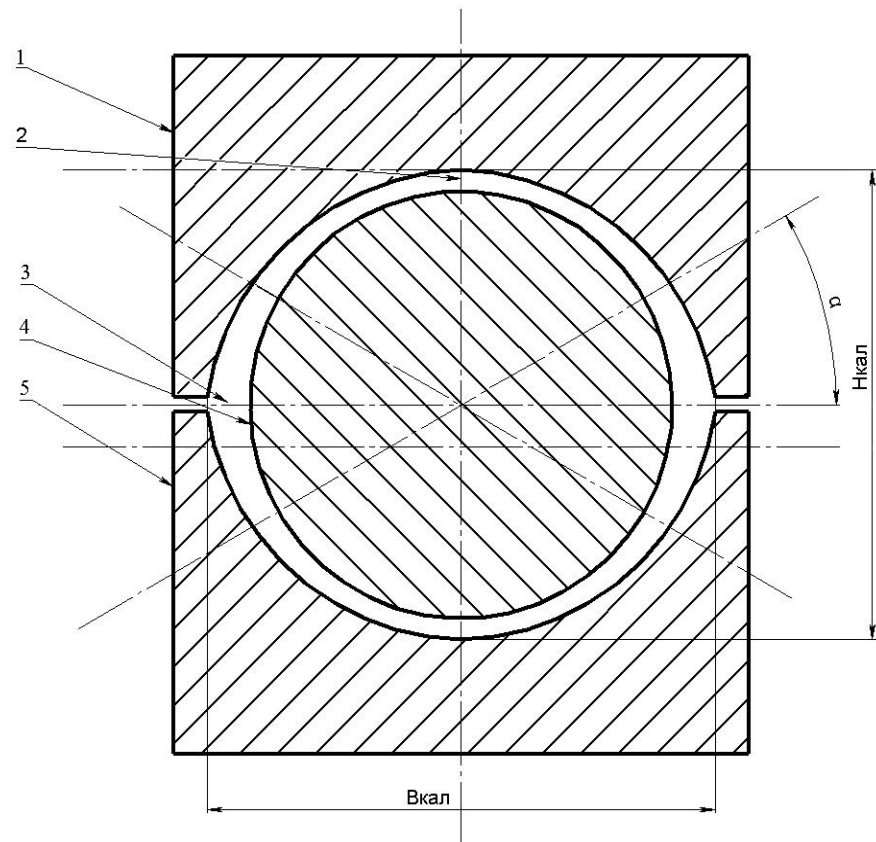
Поперечний переріз рівчака калібру та труби на початку зони обтиснення: 1 – калібр, що створений верхнім прокатним валком; 2 – вершина калібру; 3 – випуск; 4 – оправка; 5 – калібр, що створений нижнім прокатним валком; α – кут випуску; $H_{\text{кал}}$ – висота калібру; $B_{\text{кал}}$ – ширина калібру
